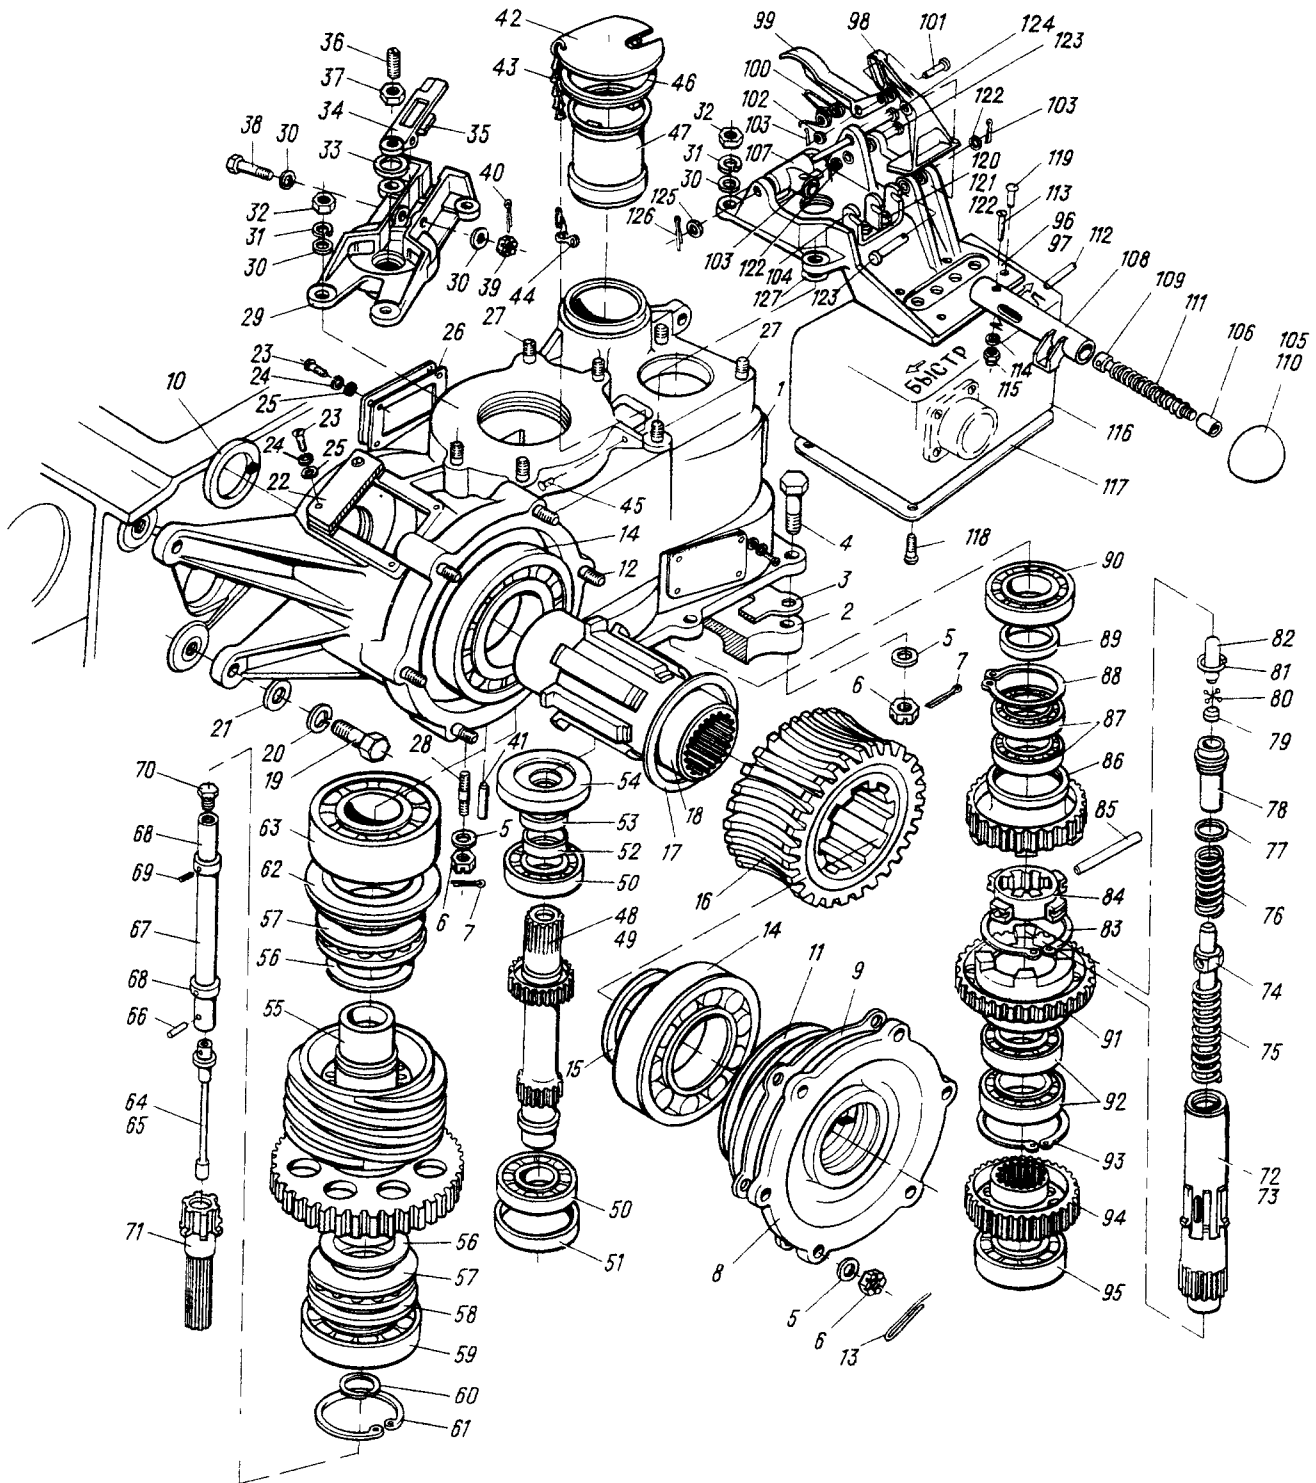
РЕДУКТОР ГИДРОПРИВОДА ТРАНСПОРТЕРА
